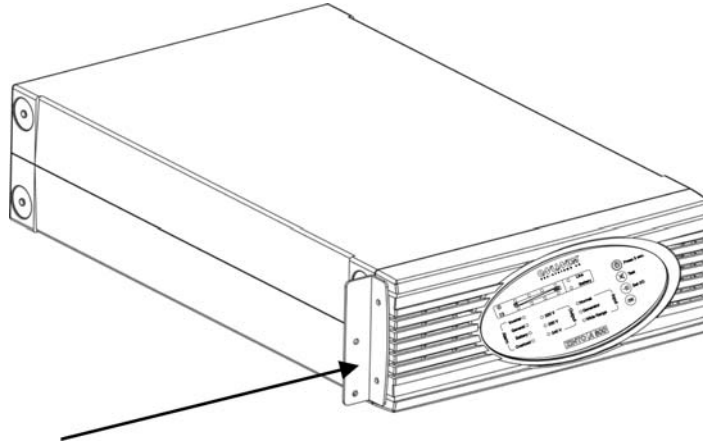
Montaggio in rack ZINTO A 800, ZINTO A 1000 – Passo 1
